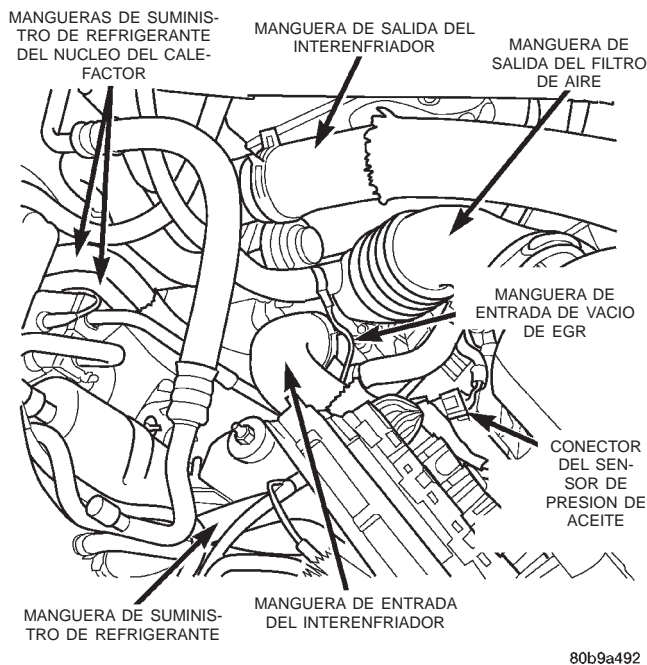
Compartimiento del motor, Volante a la izquierda — Diesel
